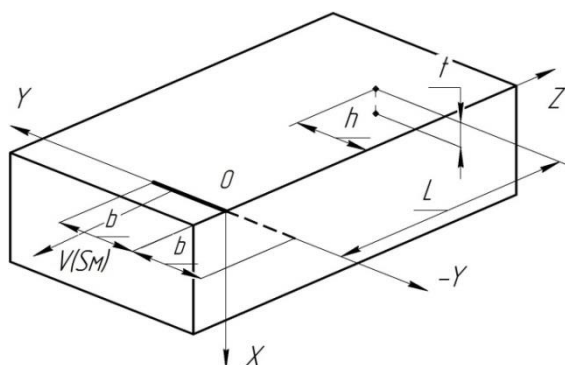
Розрахункова схема для лінійного джерела нагрівання
